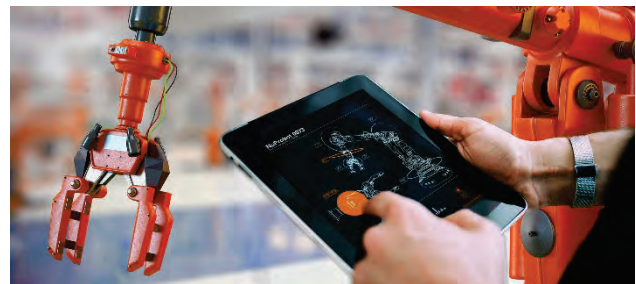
digitaler Zwilling macht Ort einer Maschinenstörung sichtbar
